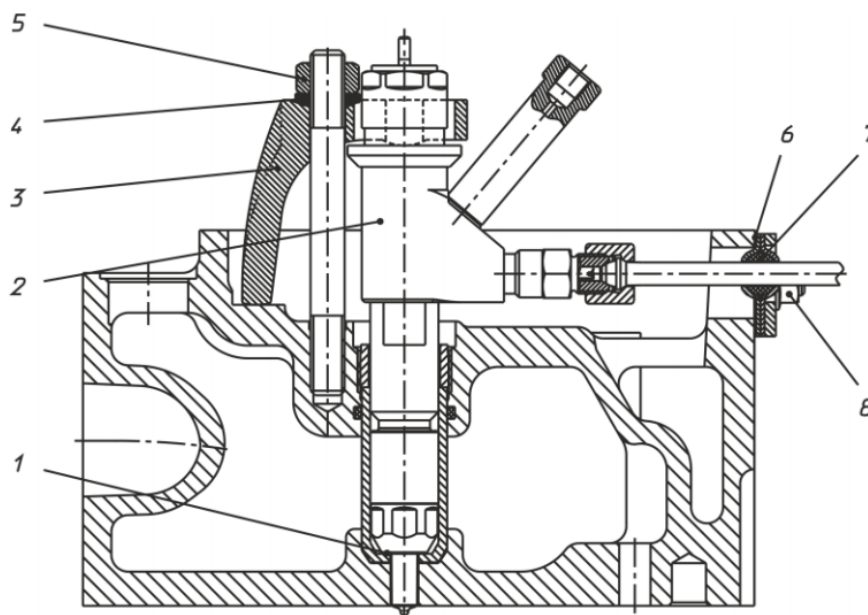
Установка форсунок: 1- шайба; 2- форсунка; 3- скоба; 4- шайба; 5-гайка; 6- прокладка переходника; 7- уплотнитель; 8- гайка.
